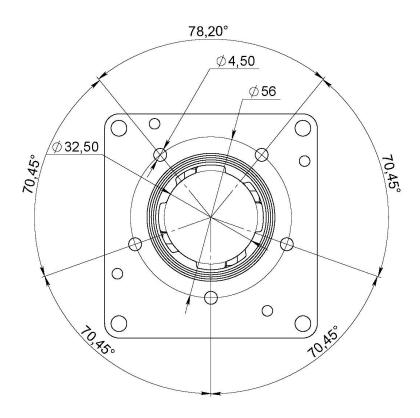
Установочные размеры. Монтаж установочной пластины
